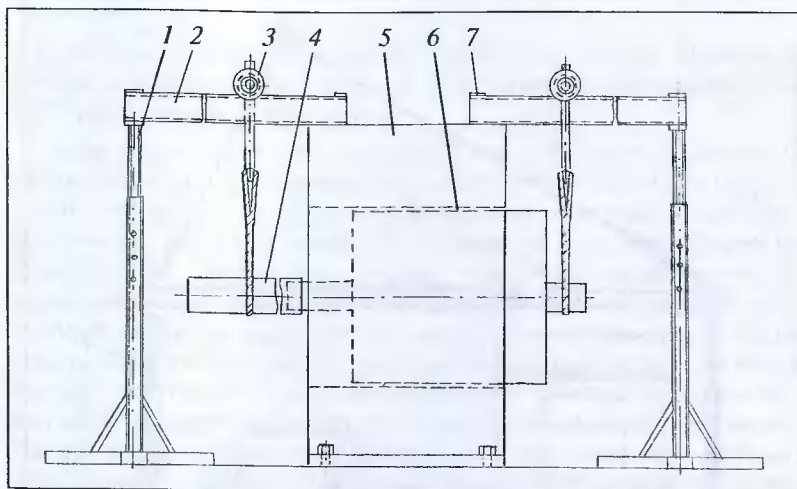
Вывод ротора электродвигателя 12 и 13-го габаритов:
